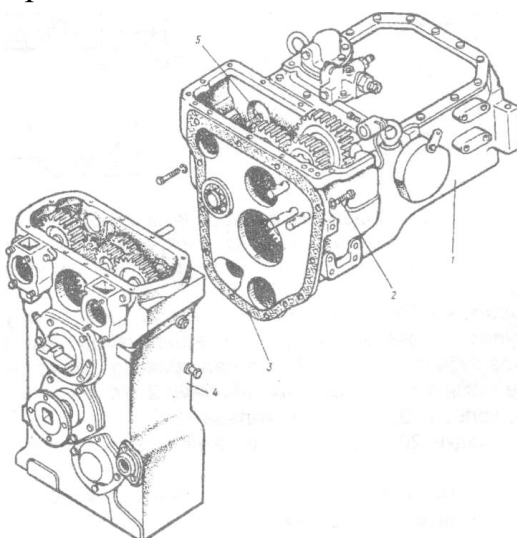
З'єднання коробки передач з роздавальною коробкою:
